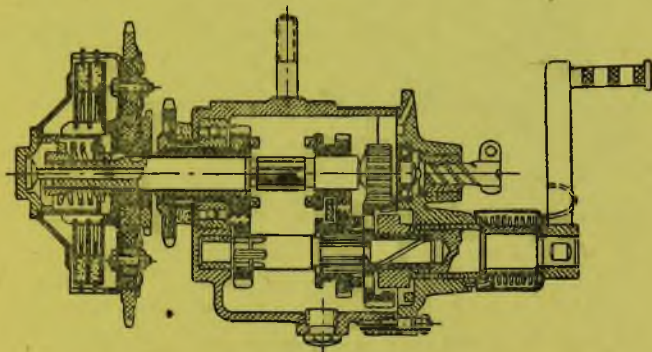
Детали муфты сцепления Л-300, ЮЖ-7, ЮЖ-8
